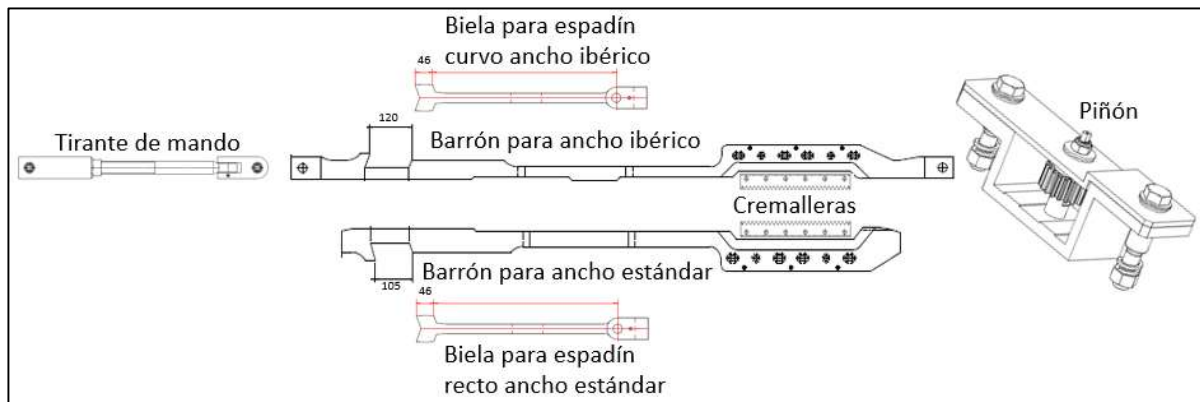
Despiece del engranaje del motor 4 del desvío D2.
